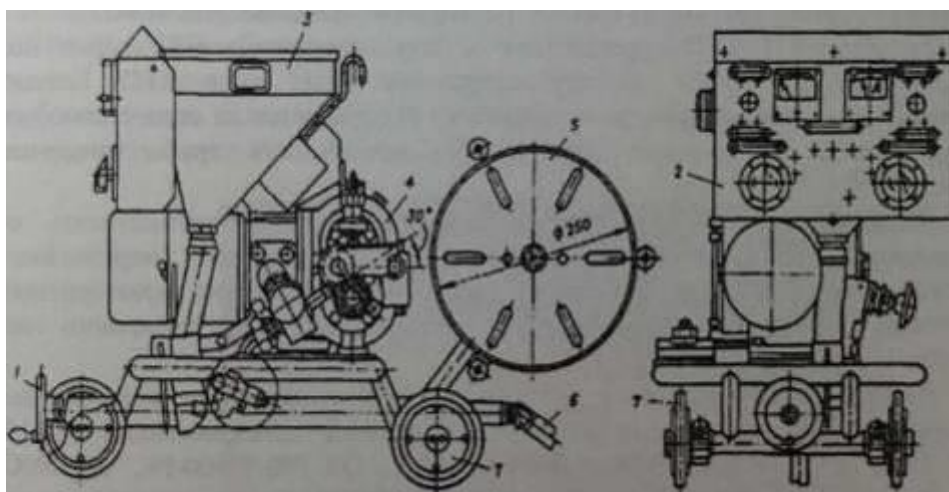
Сварочная головка СГФ-1004: 1 - корректор; 2 - пульт управления; 3 - бункер; 4 - подающий механизм; 5 - кассета; 6 - штатив; 7 - опорные ролики
